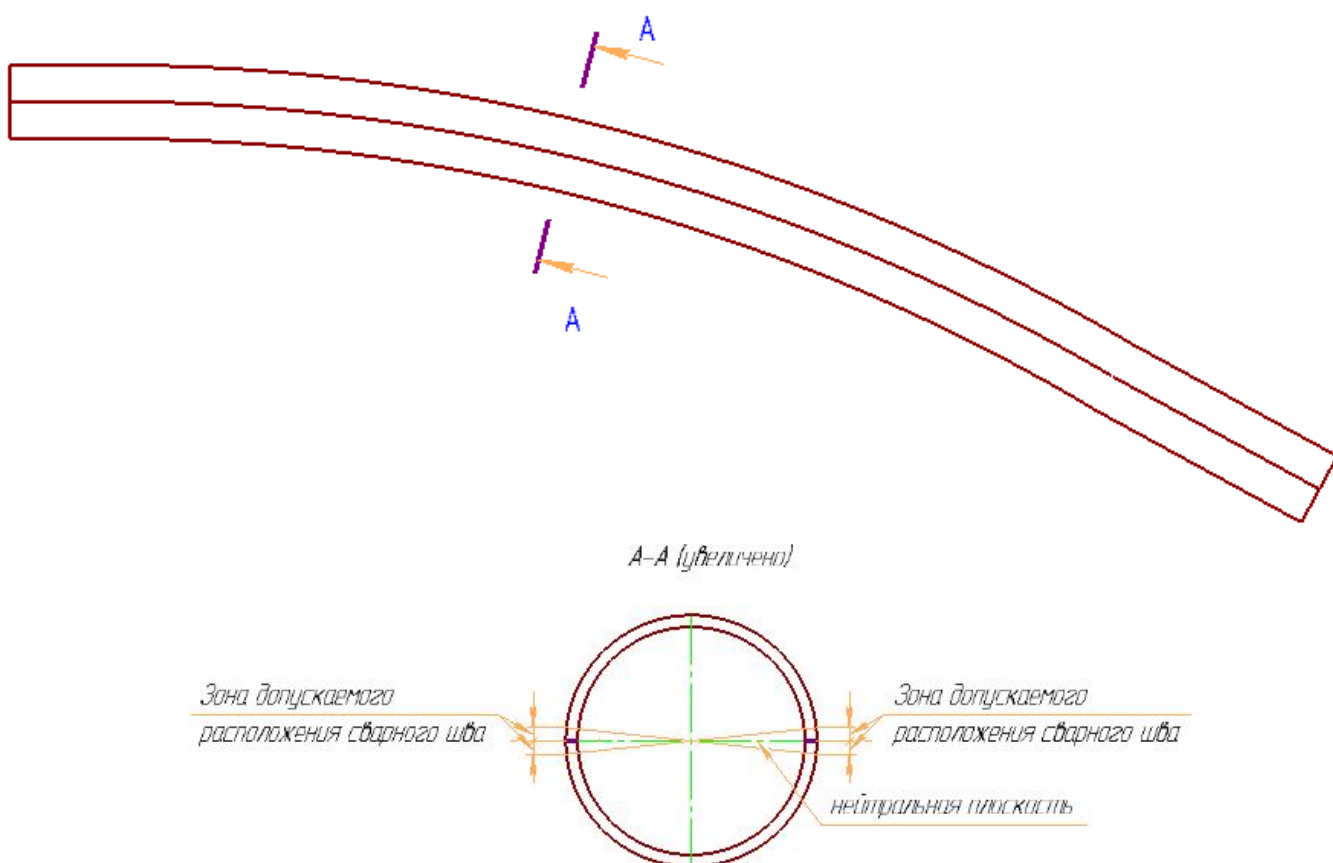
Расположения продольного сварного шва при гибке
